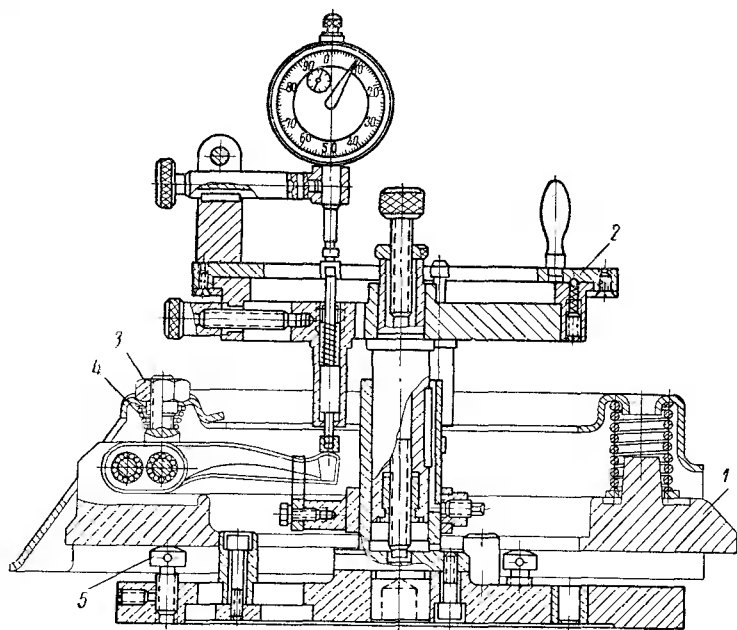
Приспособление для контроля положения рычагов выключения сцепления:
